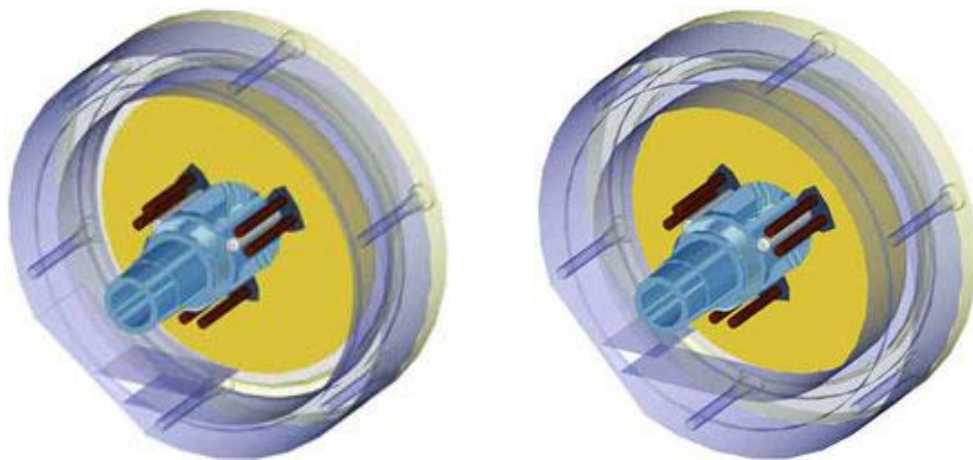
Řez rotoru bezlopatkové turbíny s jednoduchou dutou hřídelí [38]
